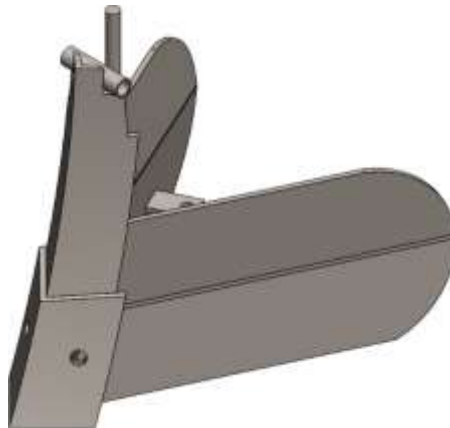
13 Apero surcador tipo vertedera alternativa B
